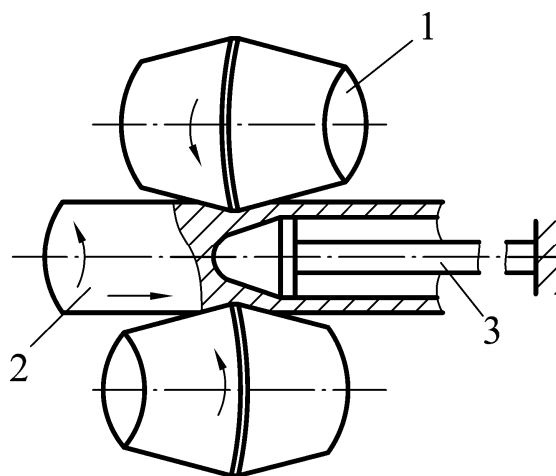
Схема прошивки заготовки при поперечно-винтовой прокатке
